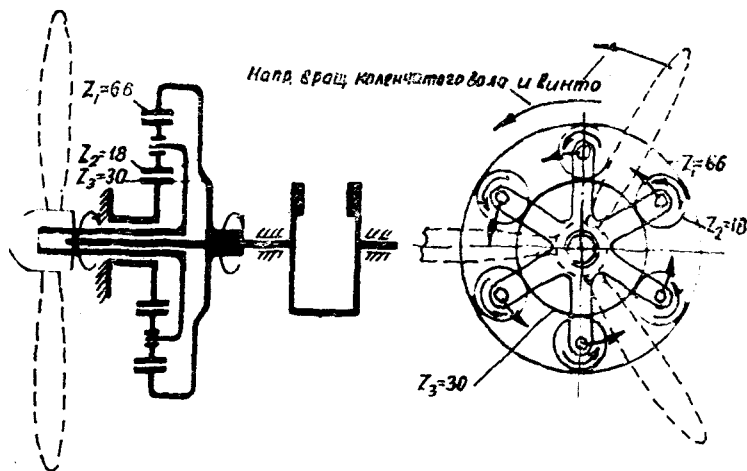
Принципиальная схема редуктора двигателя АШ-62ИР
